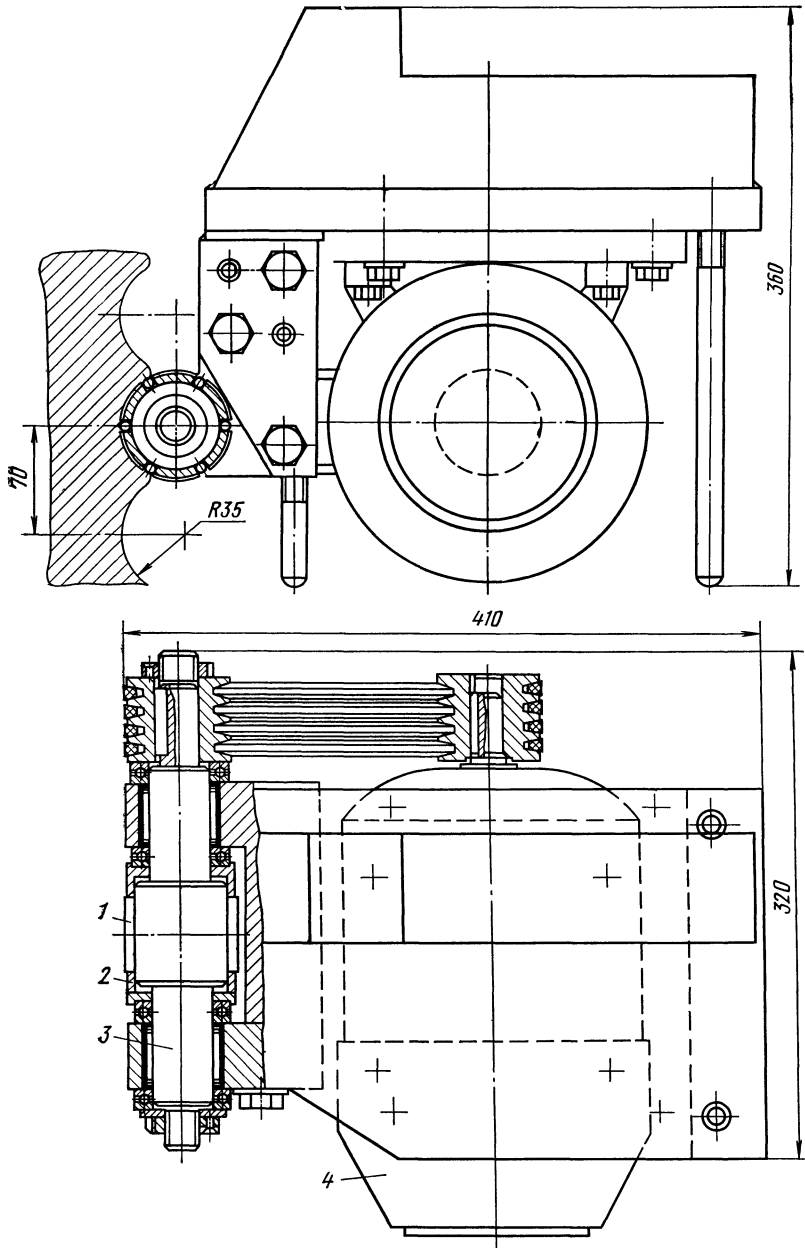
Устройство для обкатки ручьев канатных барабанов:
